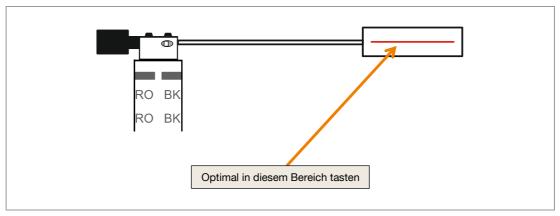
Ausrichten der Tastnadel für axiale Werkzeugabtastung
